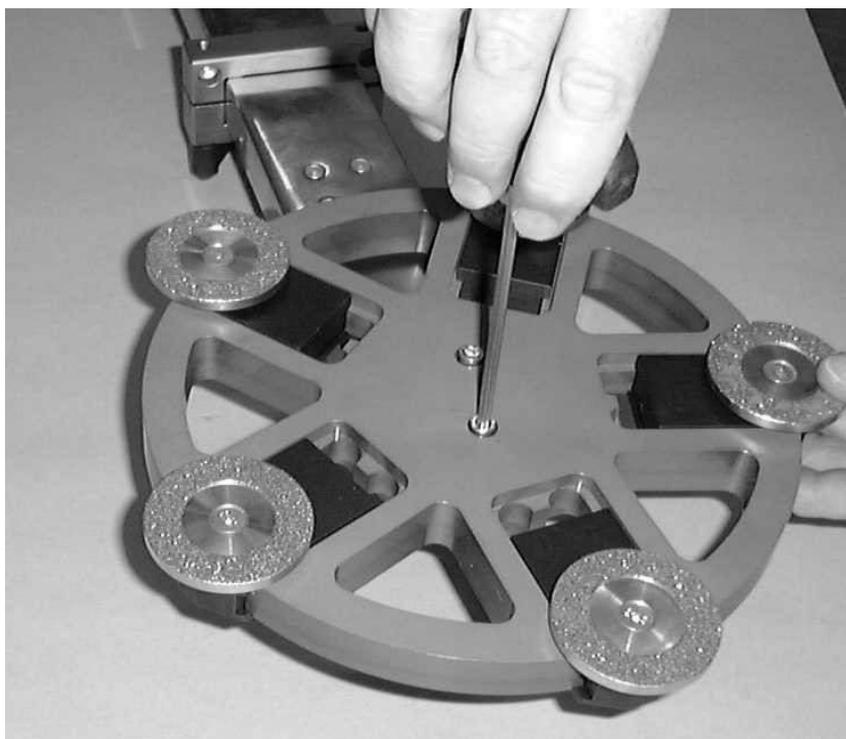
Посадка планетарного колеса на шаровое соединение
